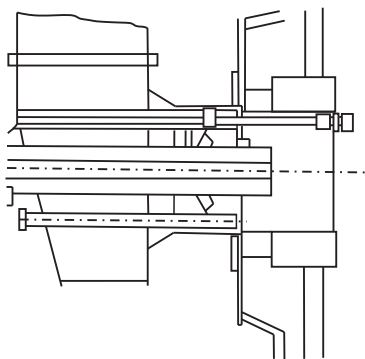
Установка горелки в корпусе котла БКЗ-160—100 ГМ
